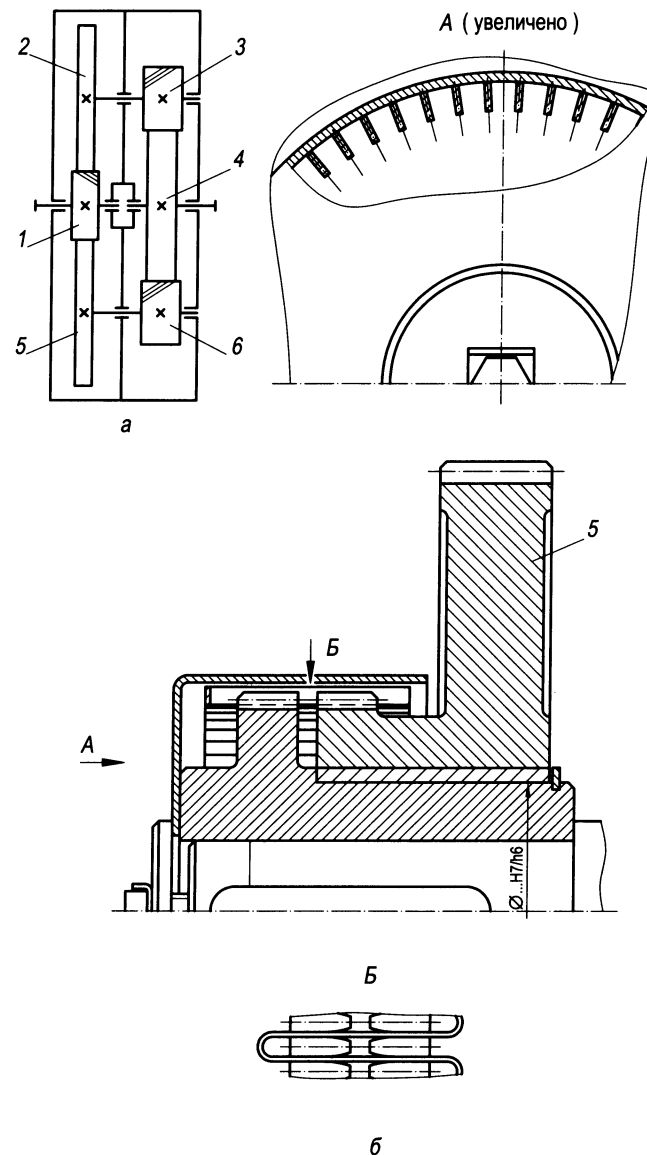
Кинематическая схема двухпоточного редуктора (а) и эскиз зубчатого колеса быстрогоходной передачи со змеевидной пружиной (б)
